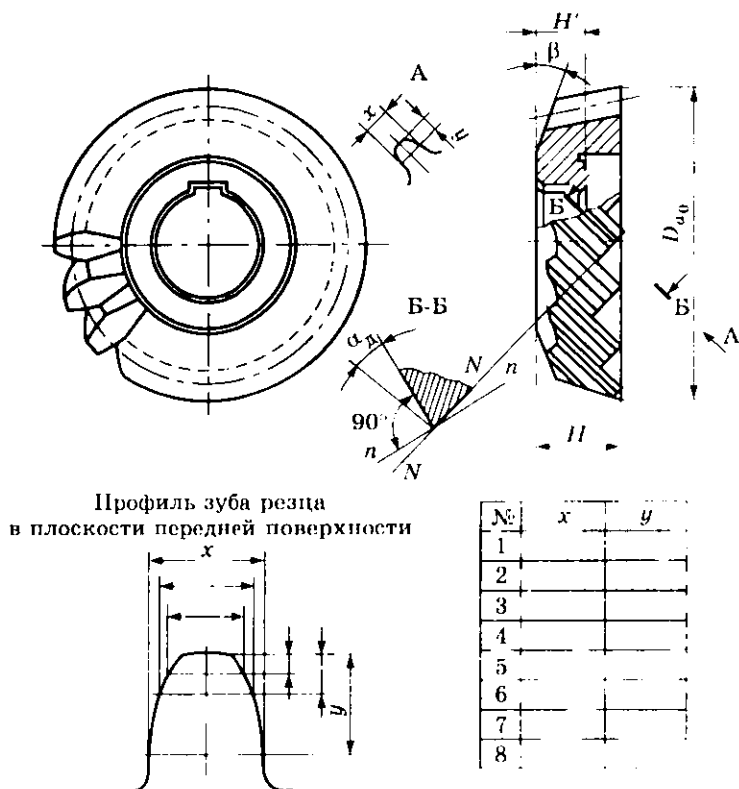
Конструктивные элементы обкаточного резца для обработки косозубого колеса
